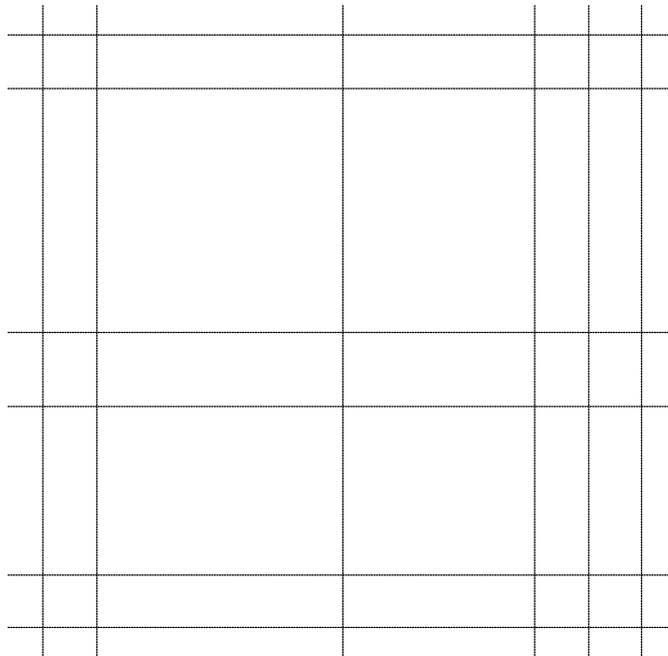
Hilfsgeometrie für die linke Seitenansicht
